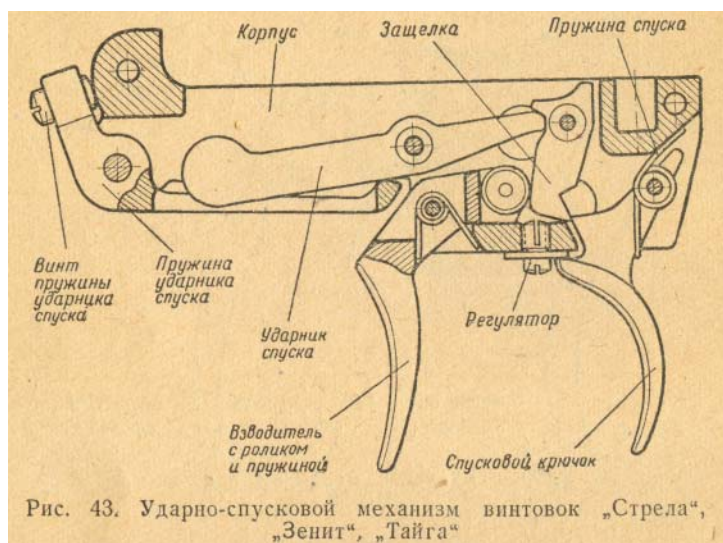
Ударно-спусковой механизм винтовок „Стрела“, „Зенит“, „Тайга“
